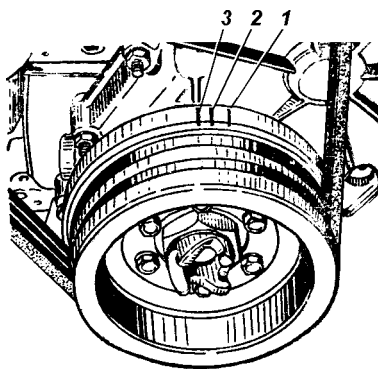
Установочные метки на шкиве коленчатого вала двигателей ЗМЗ:
